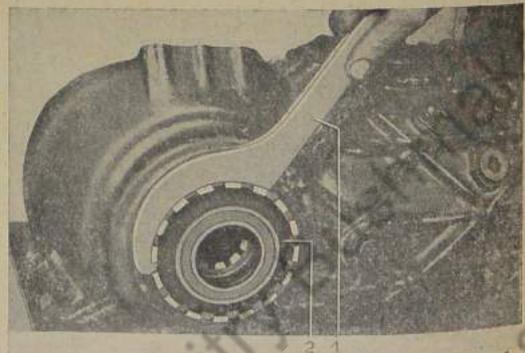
Einstellbuchse auf Tellerradseite einschrauben
